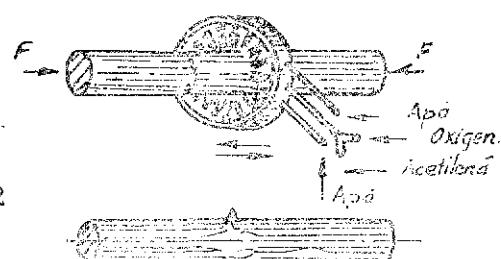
Principiul sudării prin presiune cu gaze
